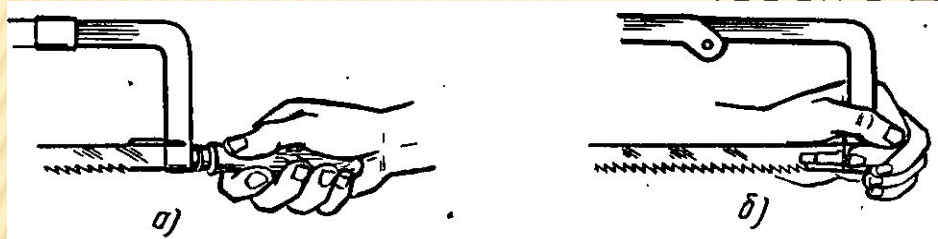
Приемы работы ножовкой при резке металла: а — положение правой руки на рукоятке, б — положение левой руки на станке.
